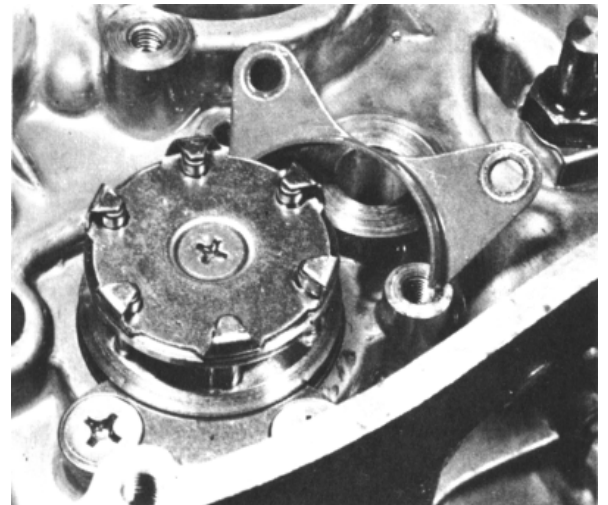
die von zwei Schrauben gehaltene Anschlagplatte wieder anbringen
